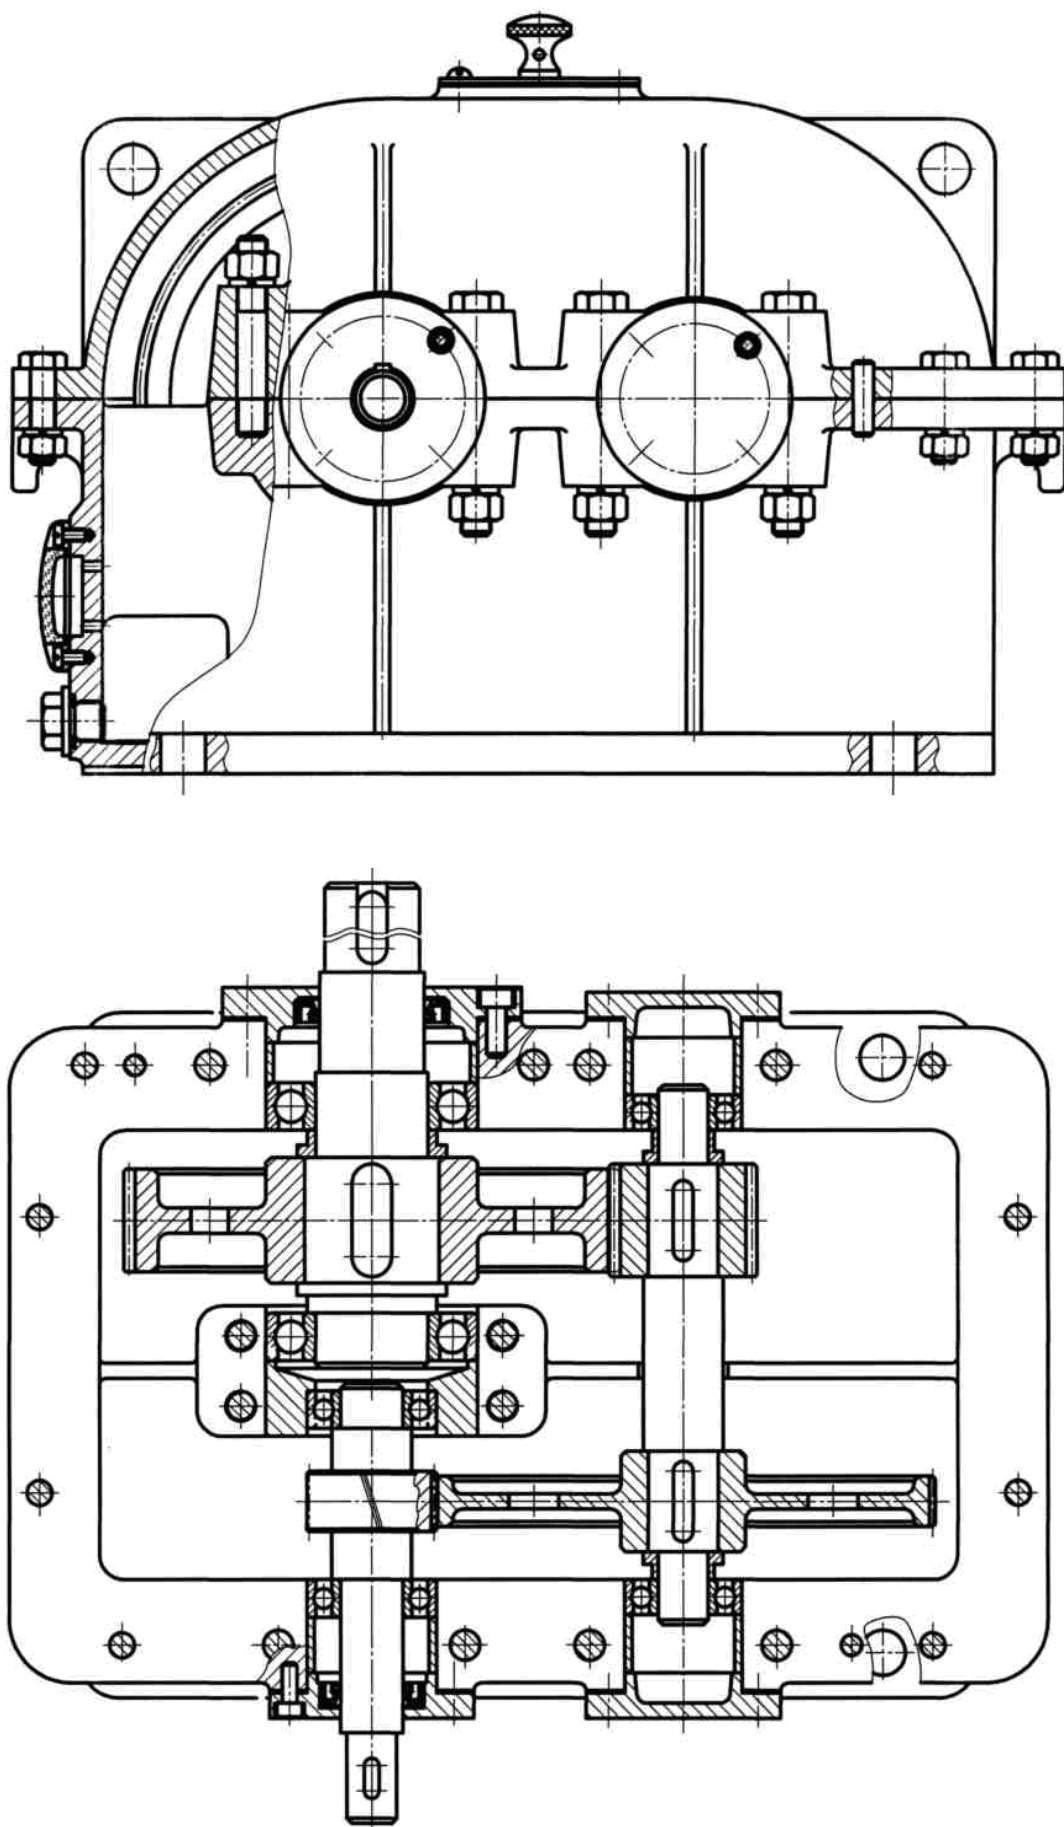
Редуктор двухступенчатый цилиндрический соосный горизонтальный
